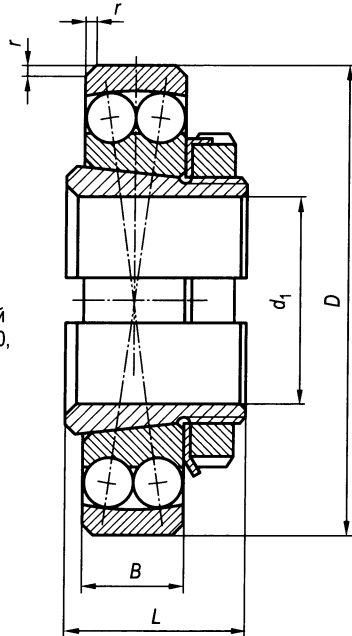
Подшипник шариковый радиальный сферический двухрядный с закрепительной втулкой серий 11200, 11300, 11500 и 11600
